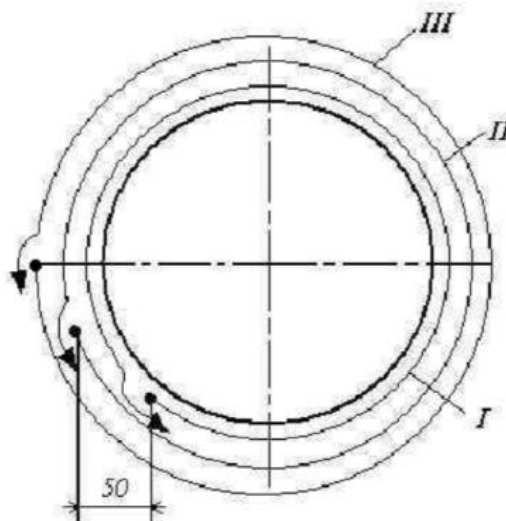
Схема зварювання різних шарів шва орбітальним аргонодуговим зварюванням
